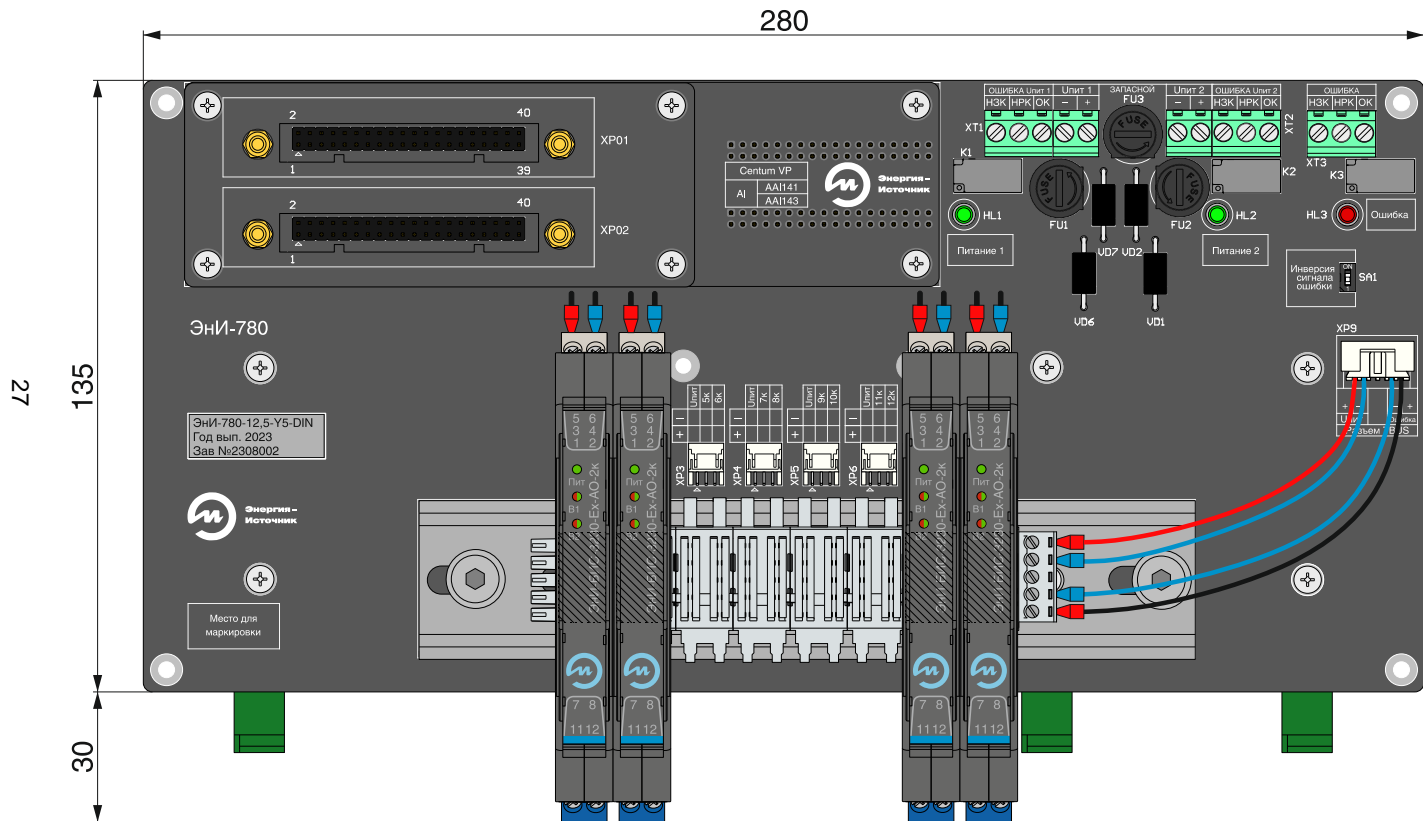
Габаритные размеры для восьми приборов с корпусом шириной 12,5 мм
